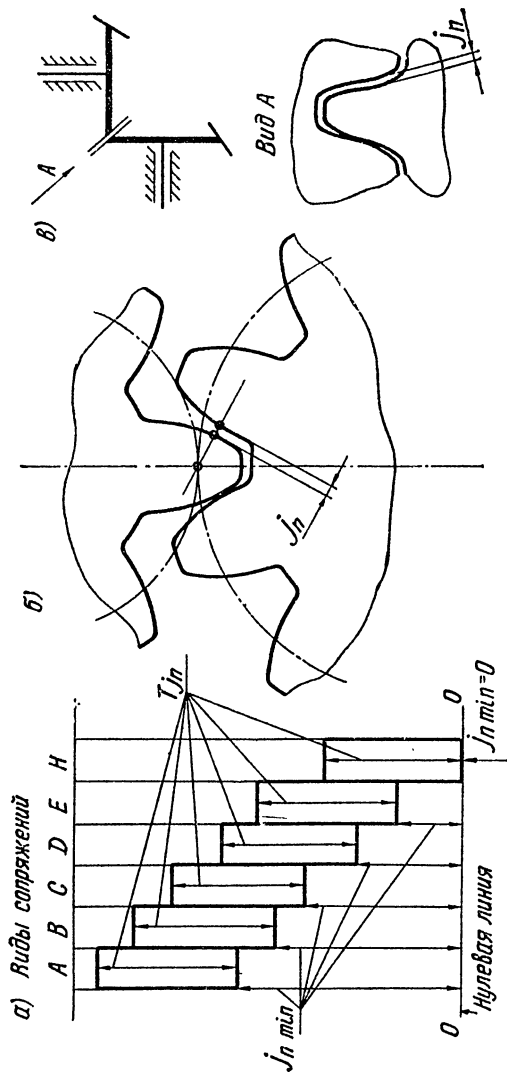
Схема расположения полей допусков: а — для принятых видов сопряжений зубчатых колес; б — боковой зазор в цилиндрических передачах; а — в конических передачах
